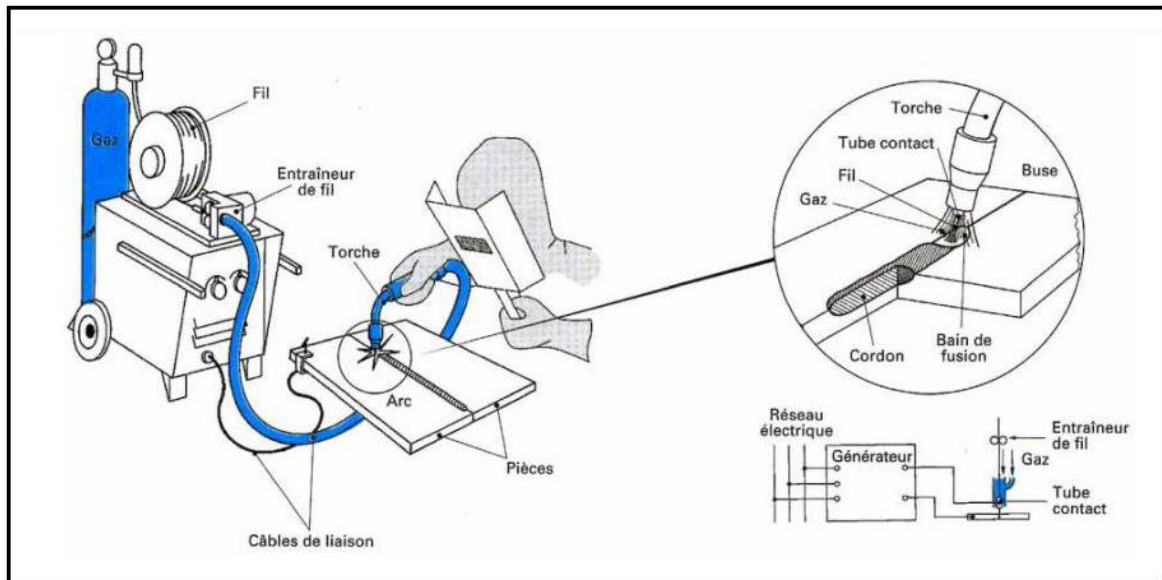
Installation type pour le soudage semi-automatique MIG/MAG [10].
